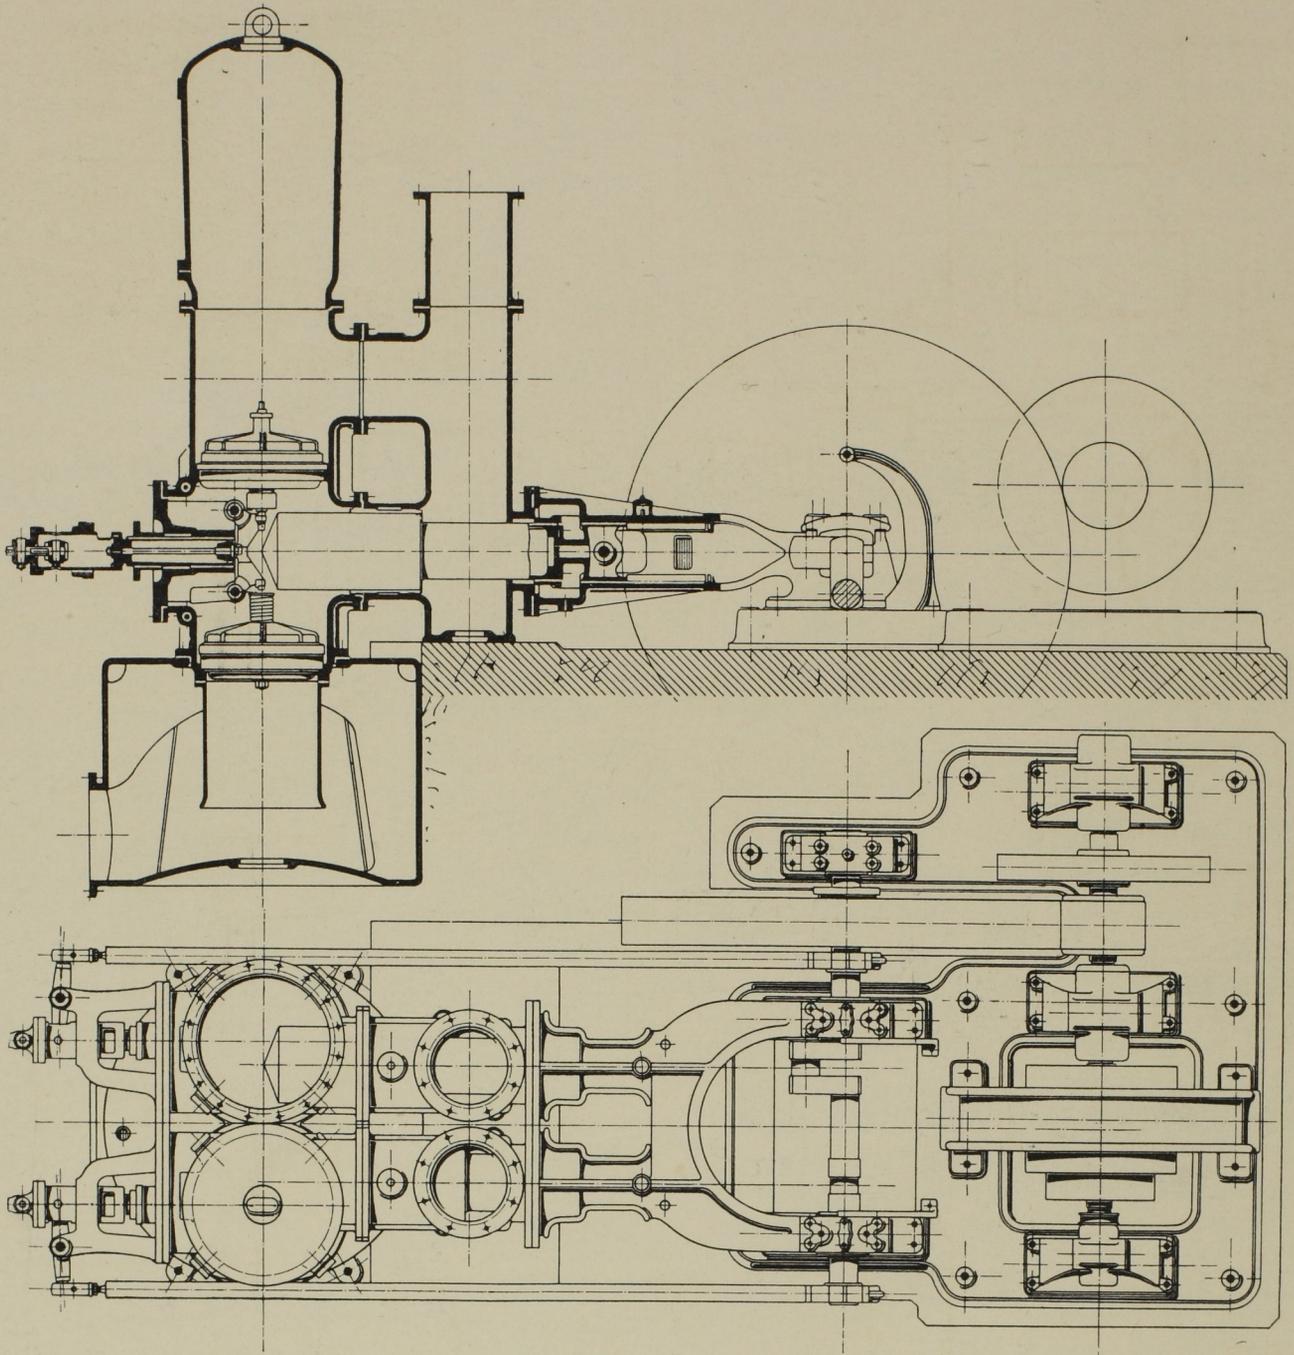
Längsschnitt und Grundriss der Pumpe.
